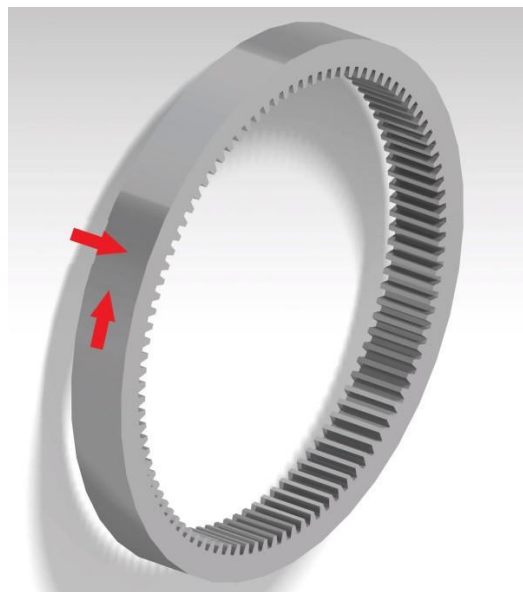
Vista en detalle del CILINDRADO_ACABADO de la cremallera (Fuente: Elaboración propia)
